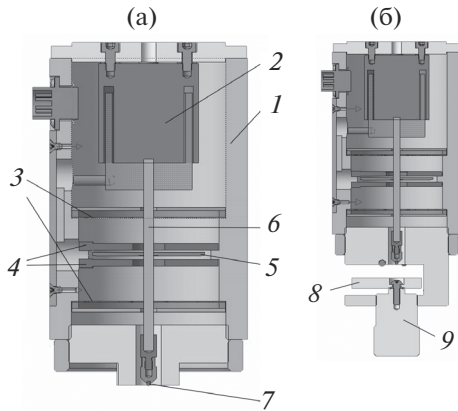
Схема портативного твердомера с насадками для измерения массивных (а) и тонких (б) образцов: 1 – корпус; 2 – актюатор; 3 – мембраны; 4 – неподвижные емкостные пластины; 5 – подвижная емкостная пластина; 6 – шток; 7 – индентор; 8 – пластина; 9 – винт-ручка.
